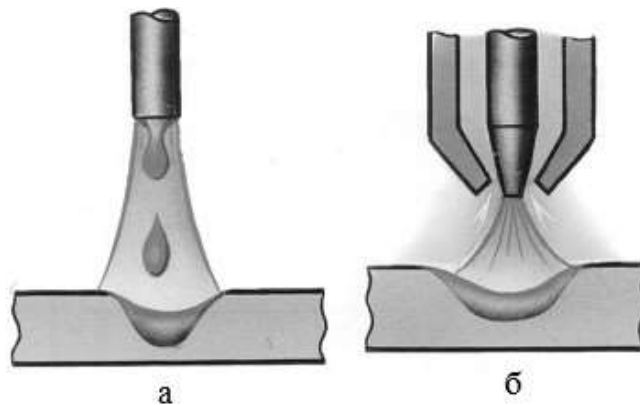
Схема зварювання плавким (а) і зварювання неплавким (б) електродами
